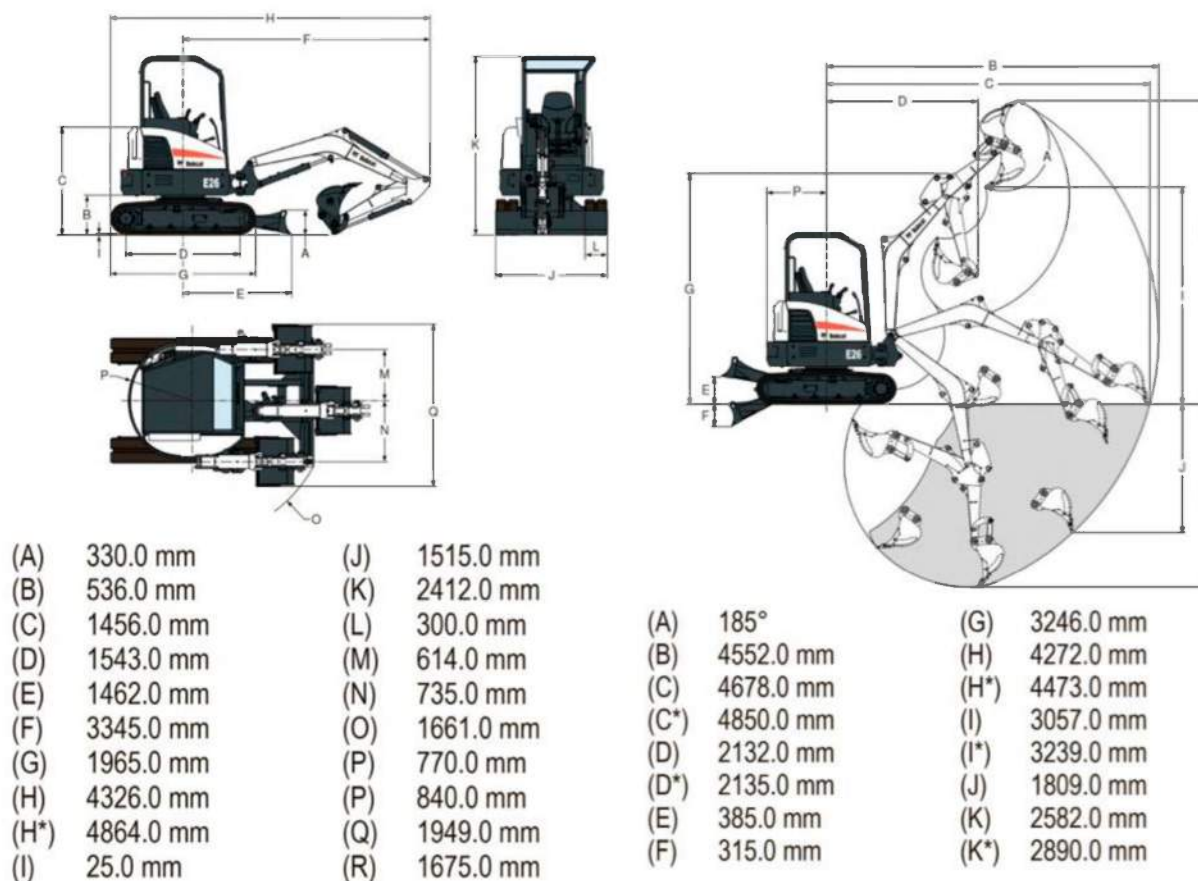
Габаритные размеры мини-экскаватора Модели Bobcat E-26
